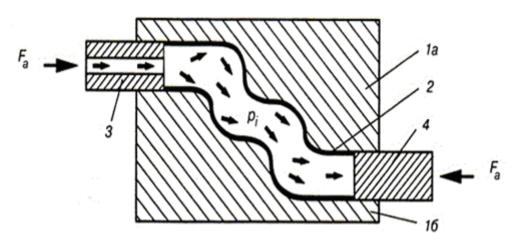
Финишная стадия процесса гидроформинга – калибровка
